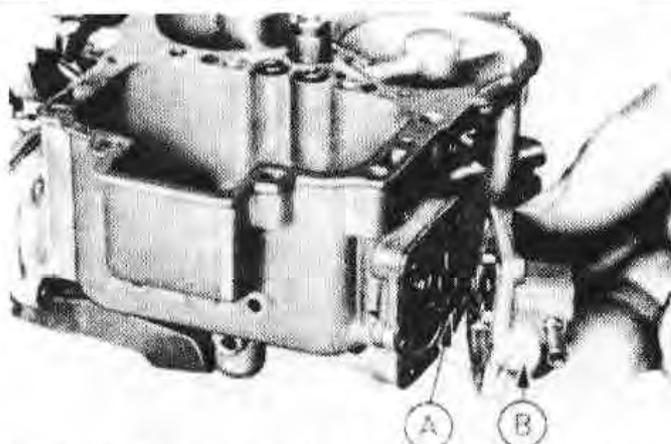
Пружина (А) и корпус (В) диафрагмы противоостановочного устройства (Разд.26)
